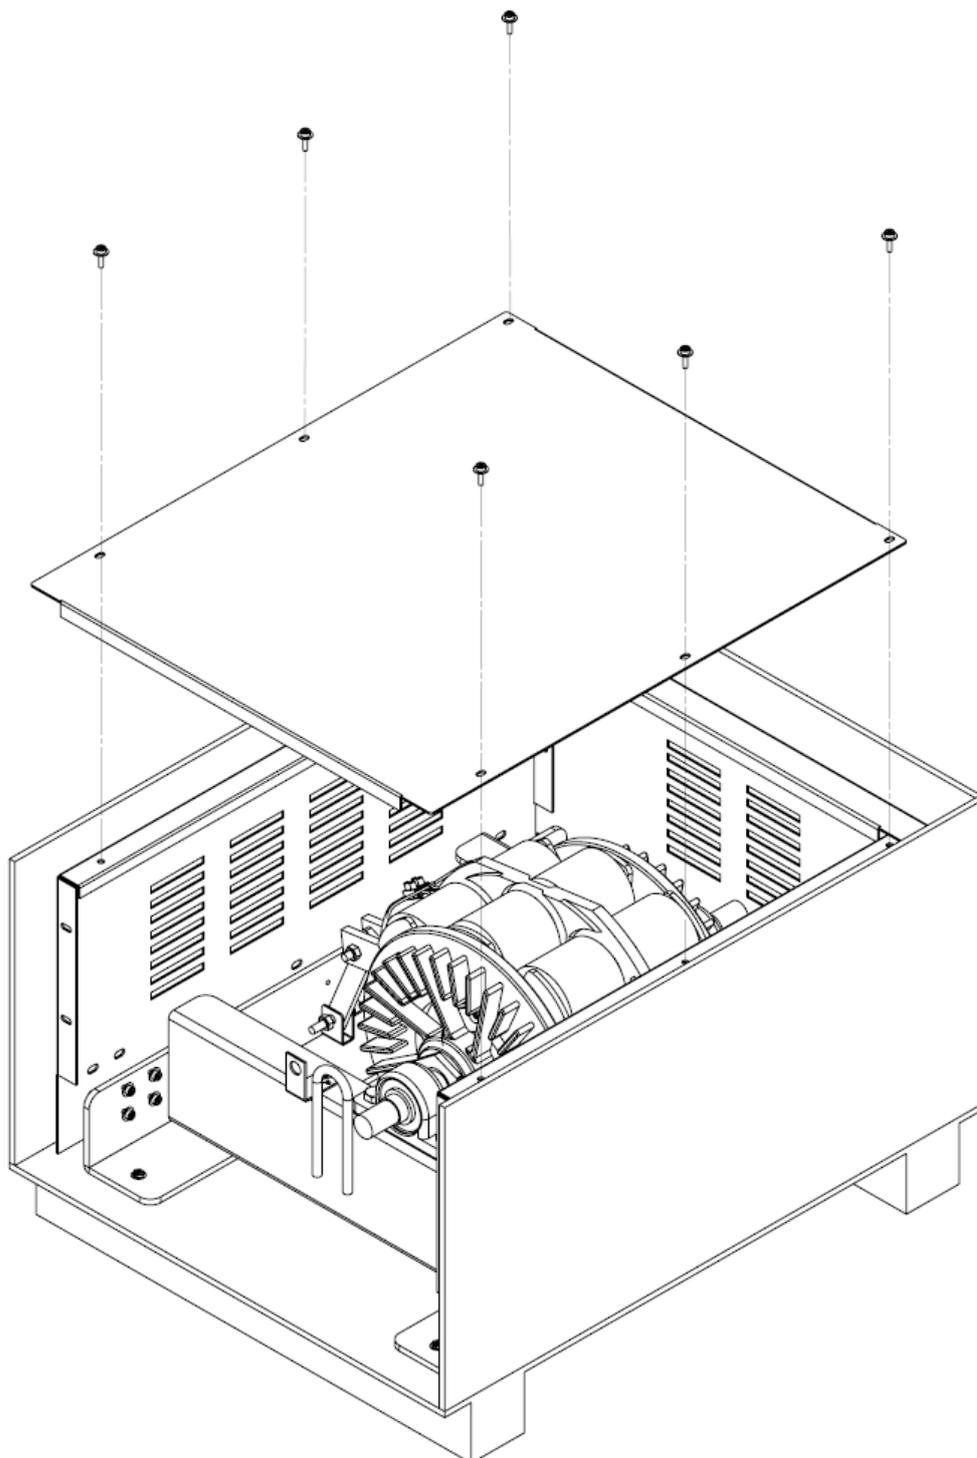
Remoção da tampa superior do Freio Eletromagnético
